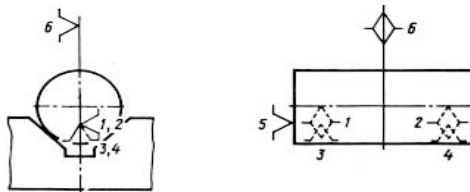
Схема базування циліндричного тіла за допомогою призм
